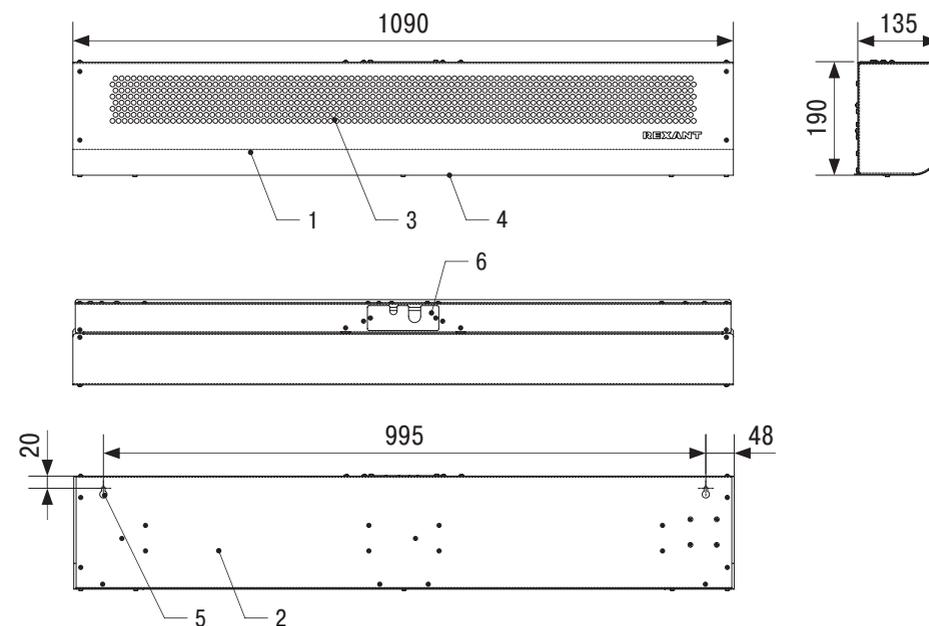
Габаритный чертеж и элементы конструкции тепловой завесы
